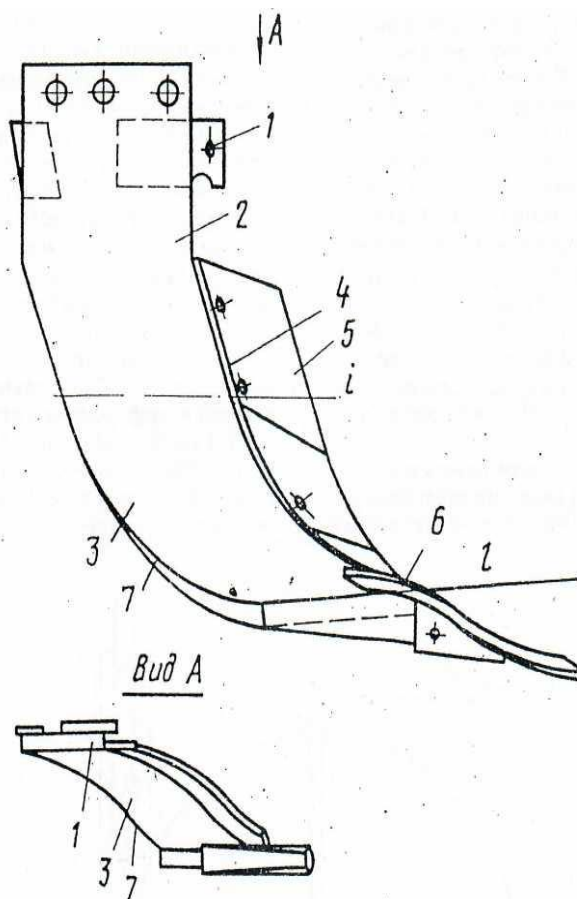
Робочий орган розпушувача [16], вид збоку
